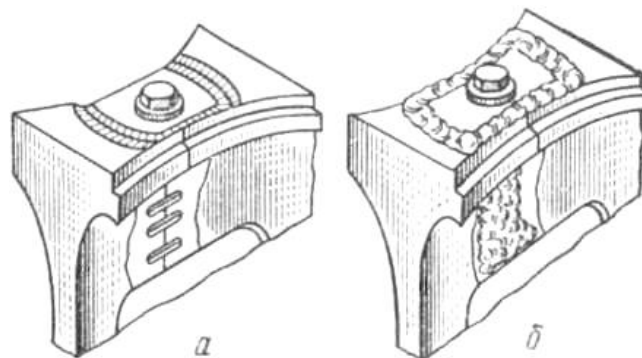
Підготовка тріщин в перемичці між циліндрами до заварки (а) і
